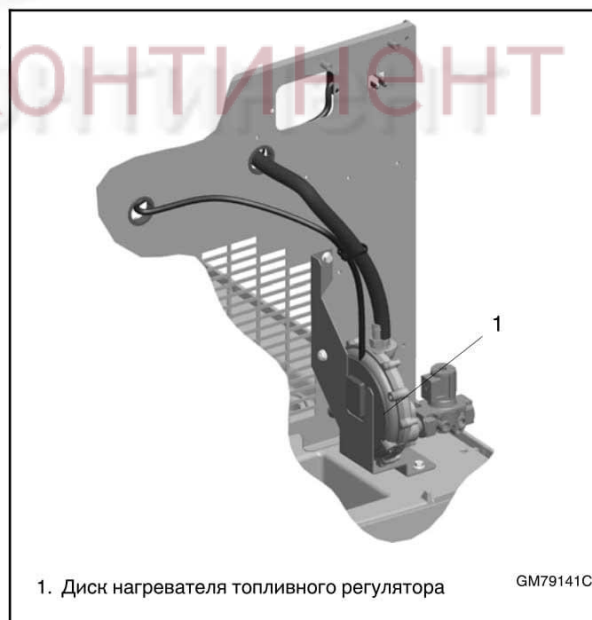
Установленный нагреватель регулятора (для RES20)
